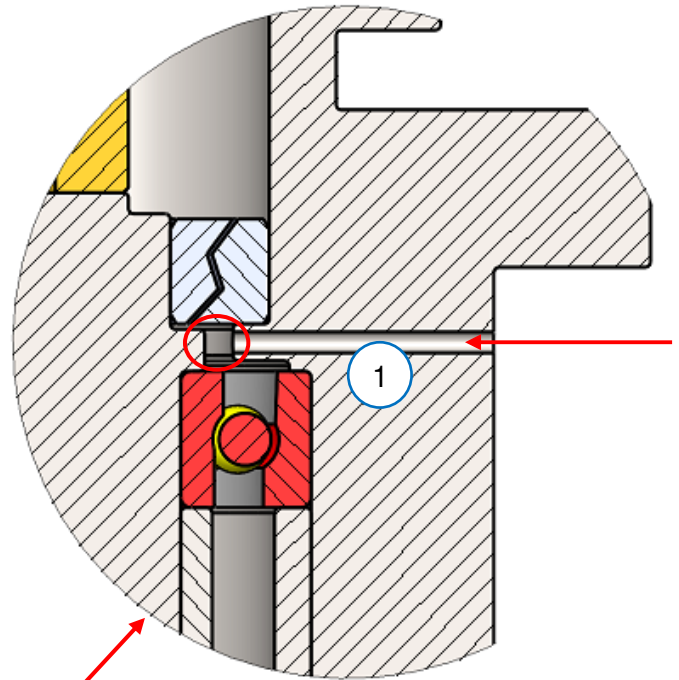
Werkzeughalter Neuauslegung Detailansicht
